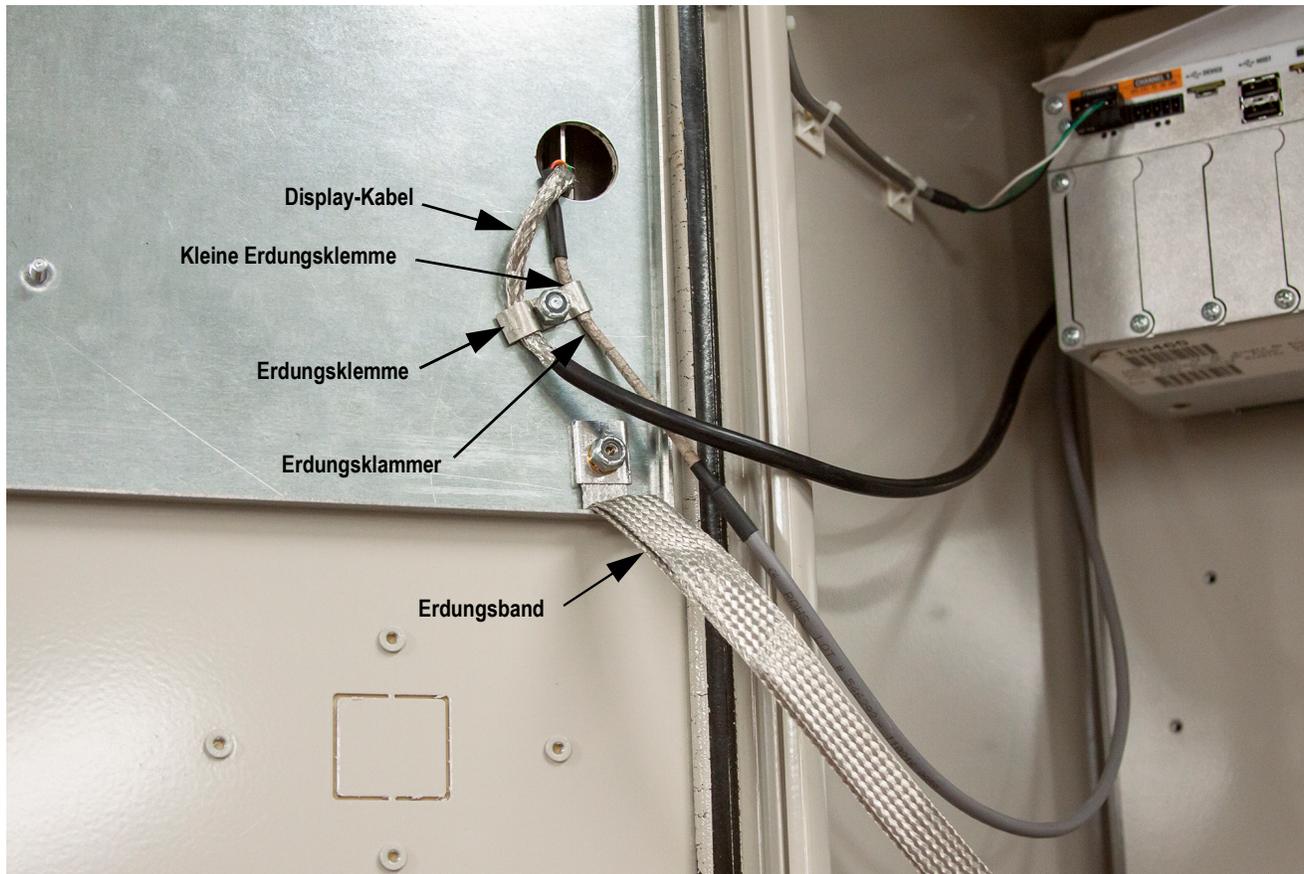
Schirmerdung für die Schalttafelmontage
